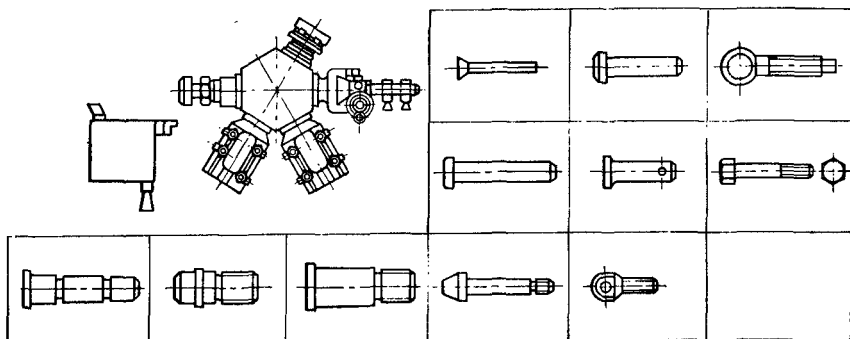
Наладка револьверного станка на изготовление различных деталей
